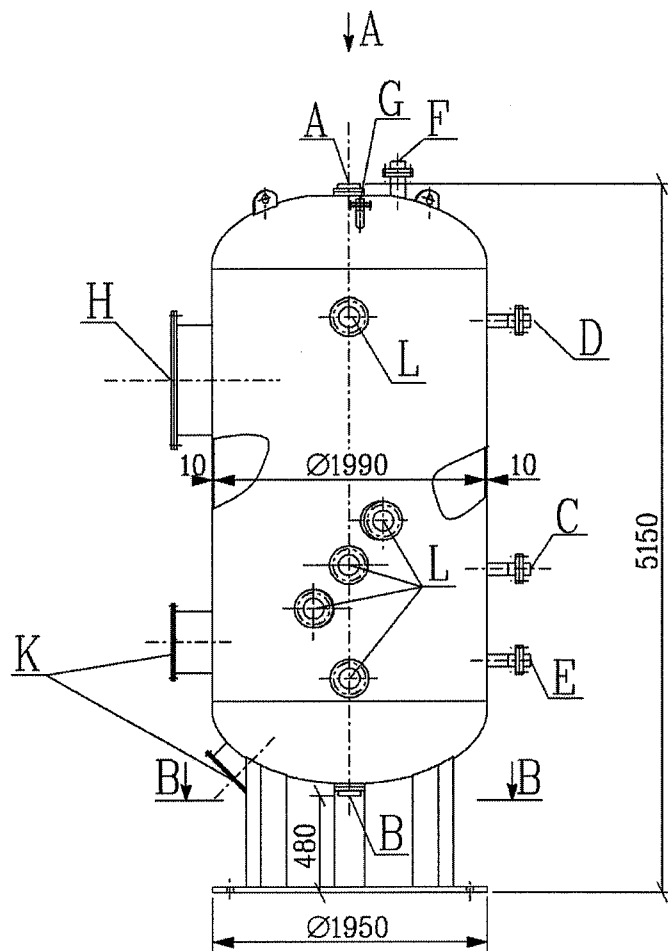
Габаритный чертеж фильтра Н-катионитного обезжелезивающего LDB11AT001, LDB12AT001
